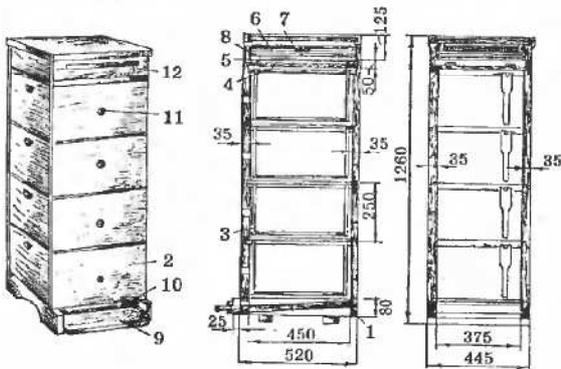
Многокорпусный улей отечественного производства (размеры в мм): внизу — общий вид, вверху — продольный и поперечный разрез; 1 — дно; 2 — корпус; 3 — рамка; 4 — потолок; 5 — подкрышник; 6 — вентиляционная рама; 7 — кровля; 8 — обвязка крыши; 9 — прилетная доска; 10 — летковый вкладыш; 11 — верхний леток; 12 — профиль для вентиляции
